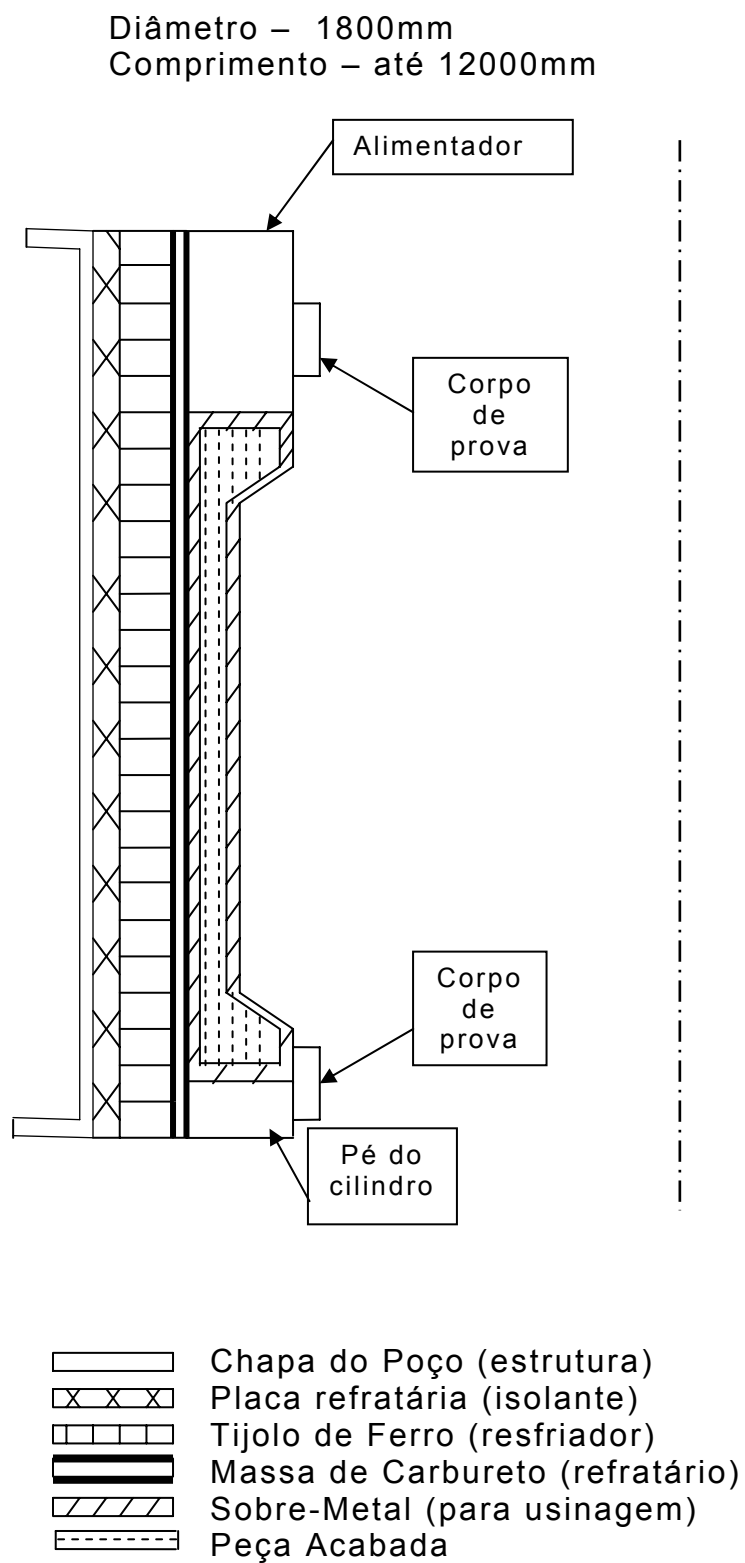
Desenho esquemático do sistema de moldagem de cilindros secadores
